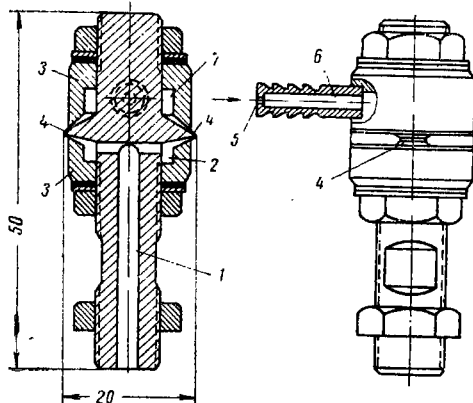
Пневматическая форсунка ЦНИИХБИ
